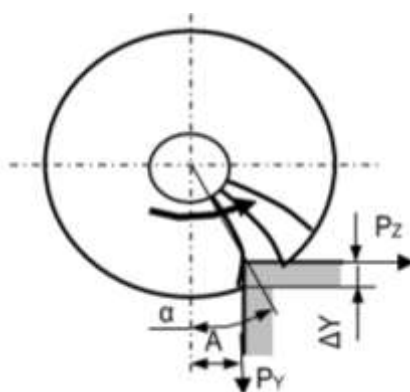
Расположение обрабатываемой кромки относительно щетки
